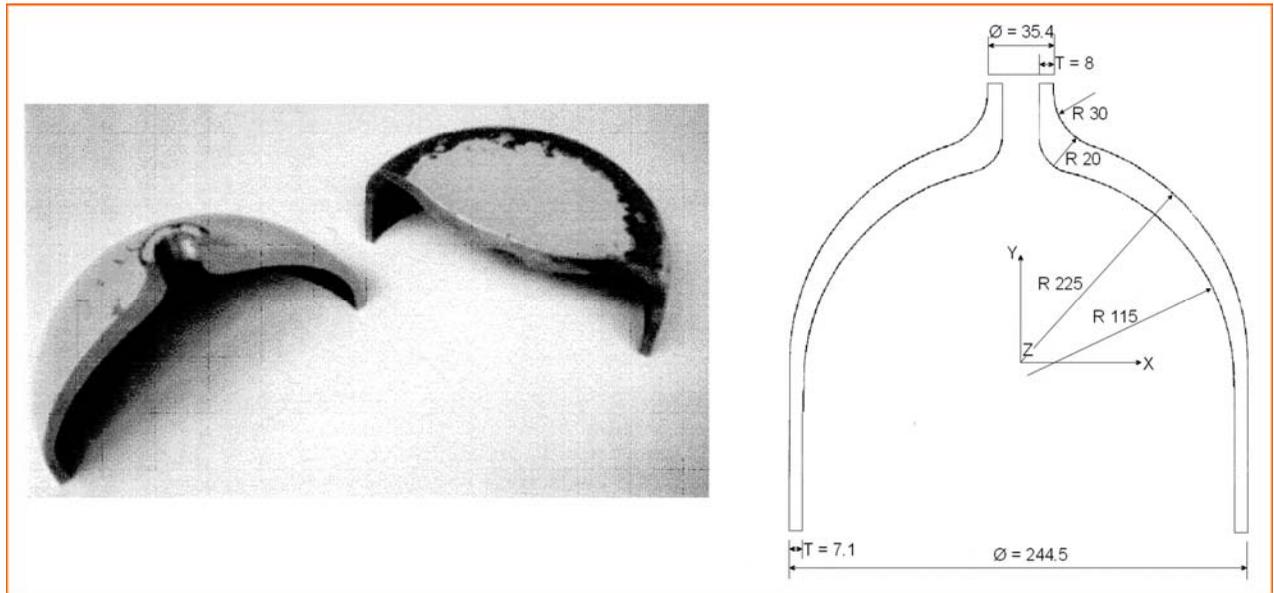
Geometría de Detalle de un tipo de Cilindro de GNC
